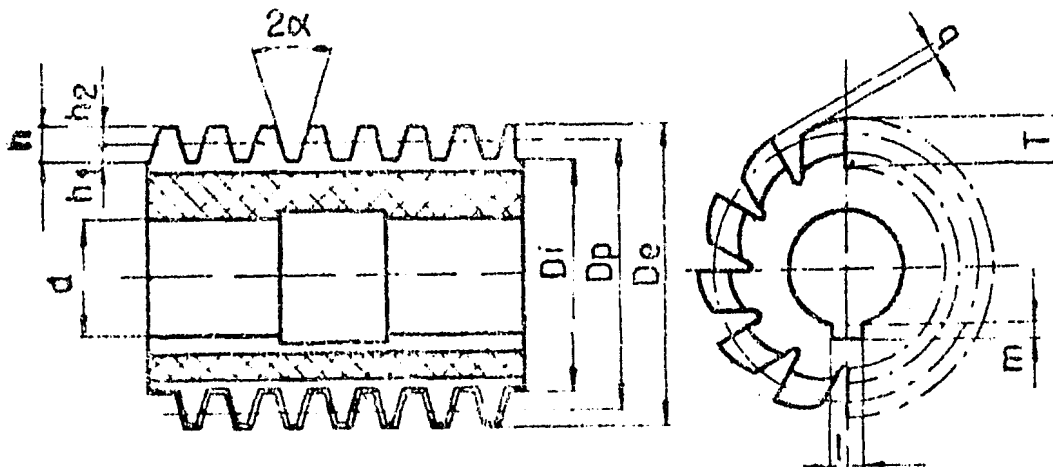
Fresa-tornillo hueca para el tallado de dientes rectos de ruedas cilíndricas.
